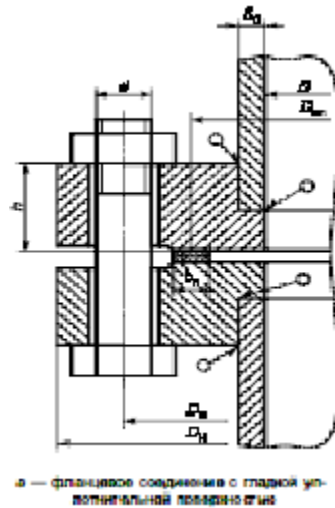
Размеры фланца с гладкой уплотнительной поверхностью
